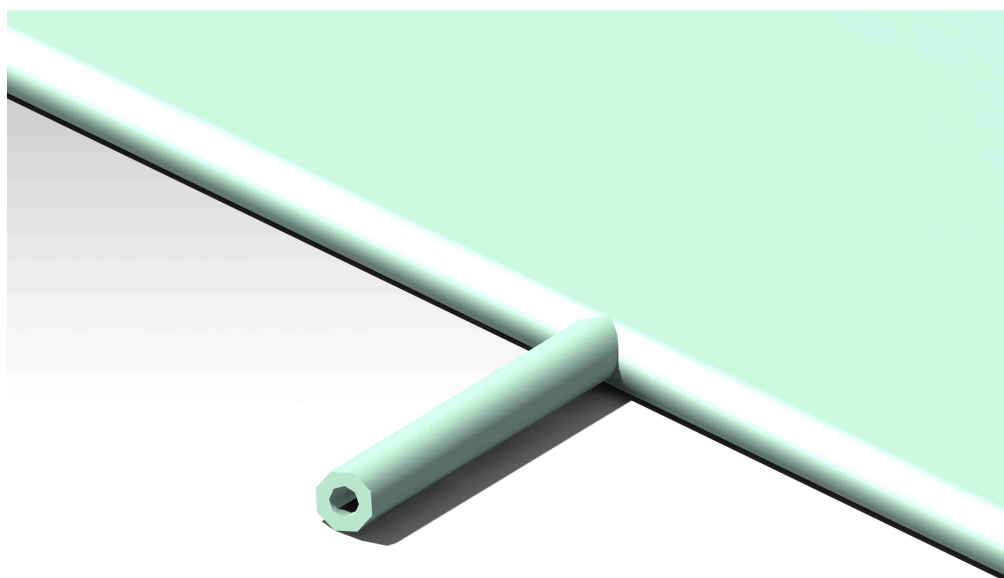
detalle boquilla bolsa para gel SILBRETT
